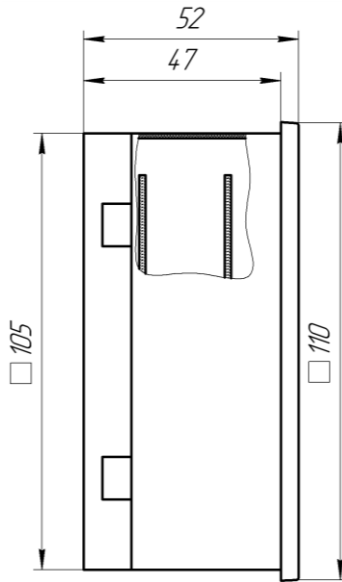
Габаритный чертеж измерителя MI-xAC (вид сбоку)
